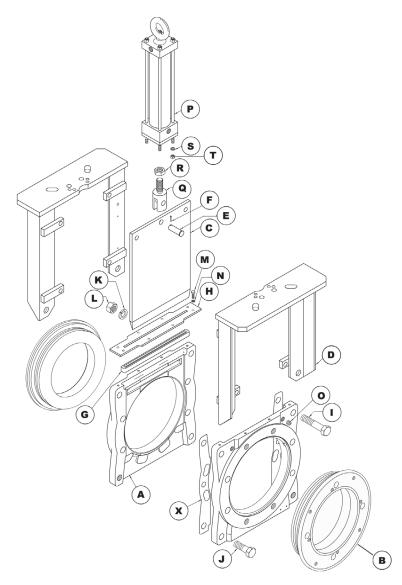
VISTA EXPLODIDA KGD-BG
